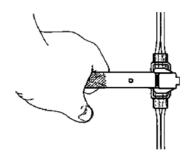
Опрессовка соединителя Е-9ВМ
